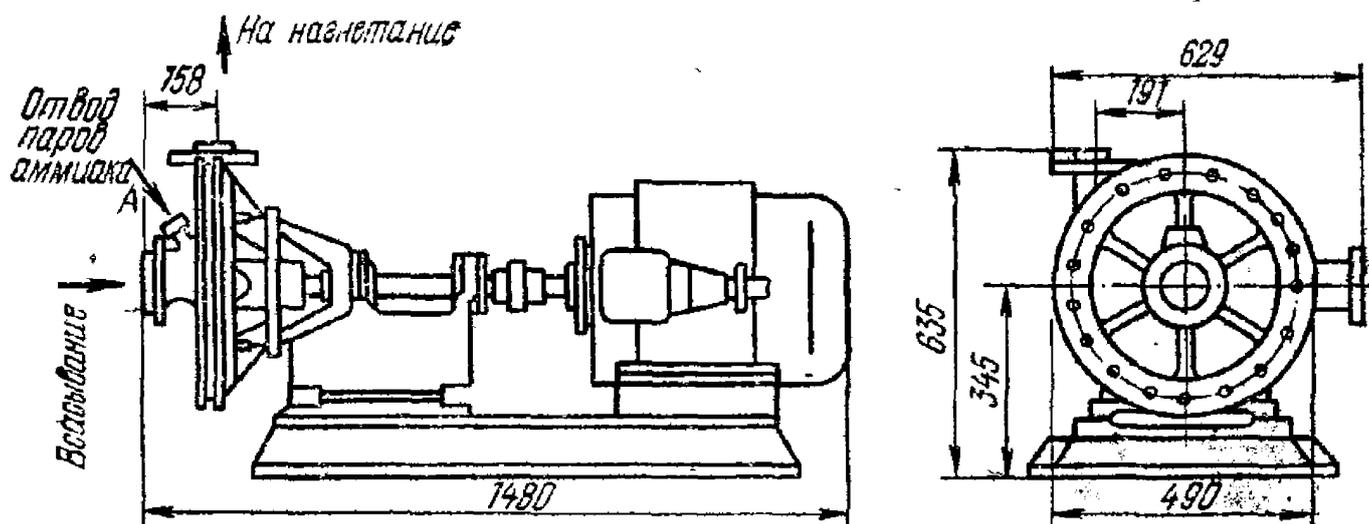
Установочный чертеж аммиачных центробежных насосов марки ЗЦ-4 и ЗЦ-4А
